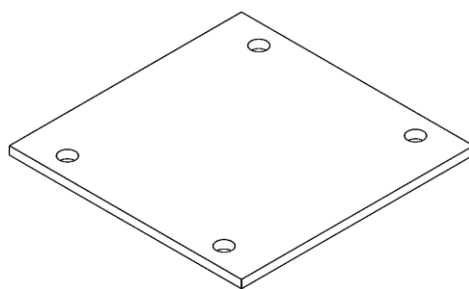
Perspetiva isométrica "Base motor CF M1 VF".
